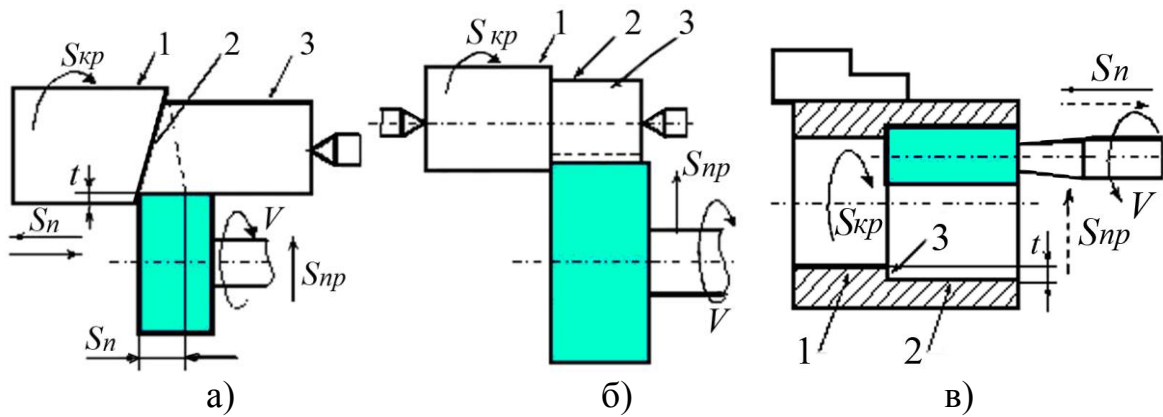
Схеми циліндричного поздовжнього, врізного та внутрішнього шліфування
